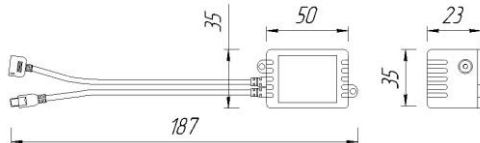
Габаритные размеры контроллера Geniled MIX GL-12V72WIR-B
